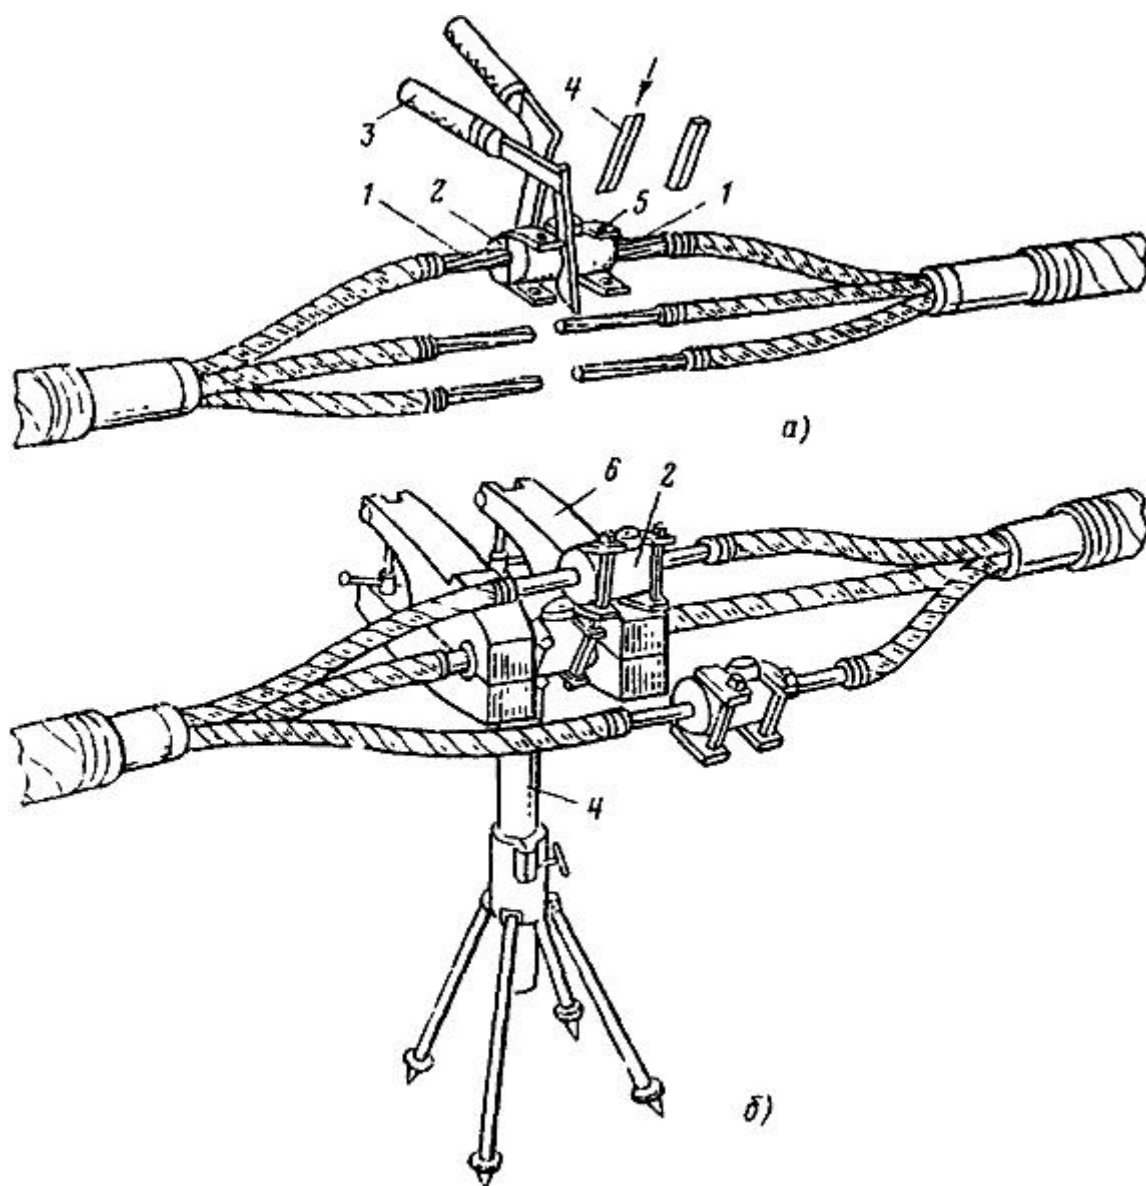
Установка сварочных форм и охладителей на жилах кабеля сечением 16-240 мм
